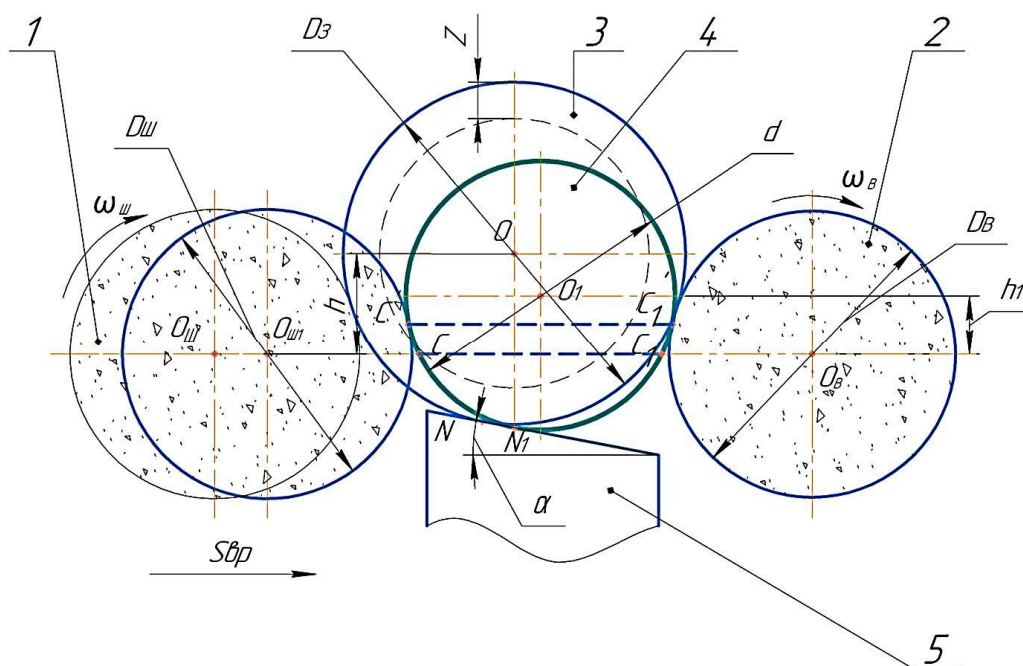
Схема врезного бесцентрового шлифования цилиндрических деталей с врезной подачей шлифовального круга (1 – шлифовальный круг; 2 – ведущий круг; 3 – обрабатываемая заготовка; 4 – обработанная деталь; 5 – опорный нож)
